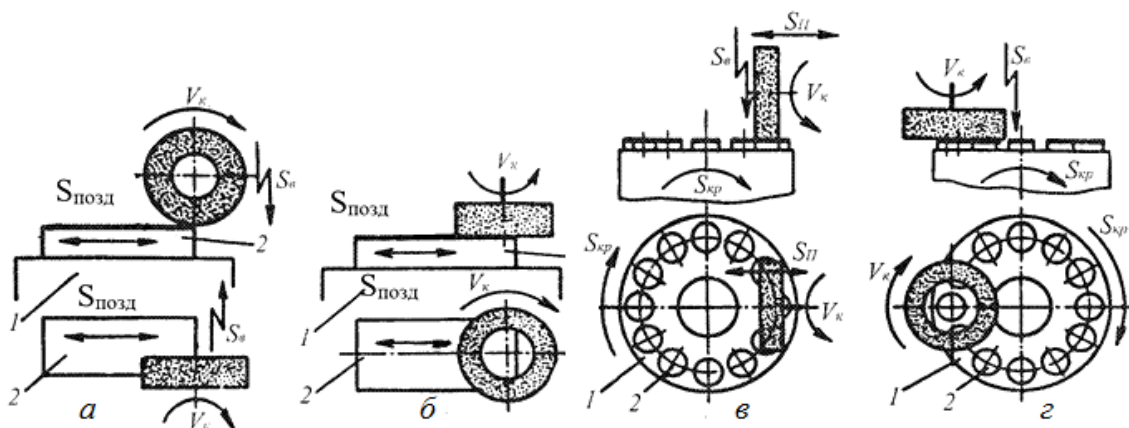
Схеми обробки заготовок на плоскошліфувальних верстатах
